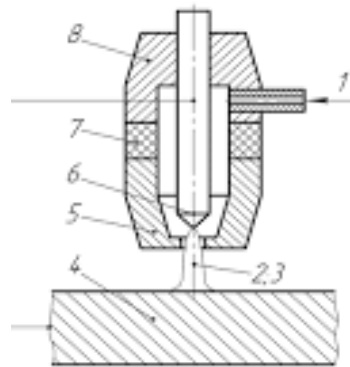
Схема плазмового зварювання: 1 - подача газу; 2- дуга; 3 - плазмовий струмінь; 4 - оброблюваний метал; 5 - наконечник; 6 - катод; 7 - ізолятор; 8 - катодний вузол
